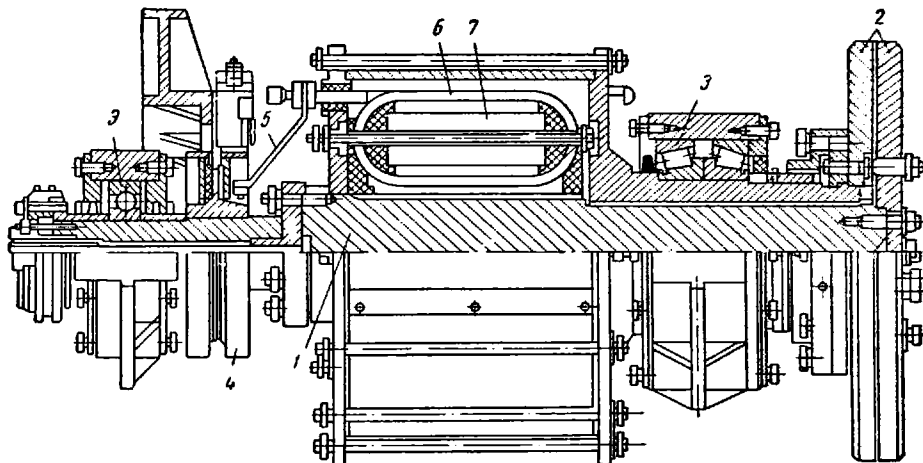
Вращающийся сварочный трансформатор:
